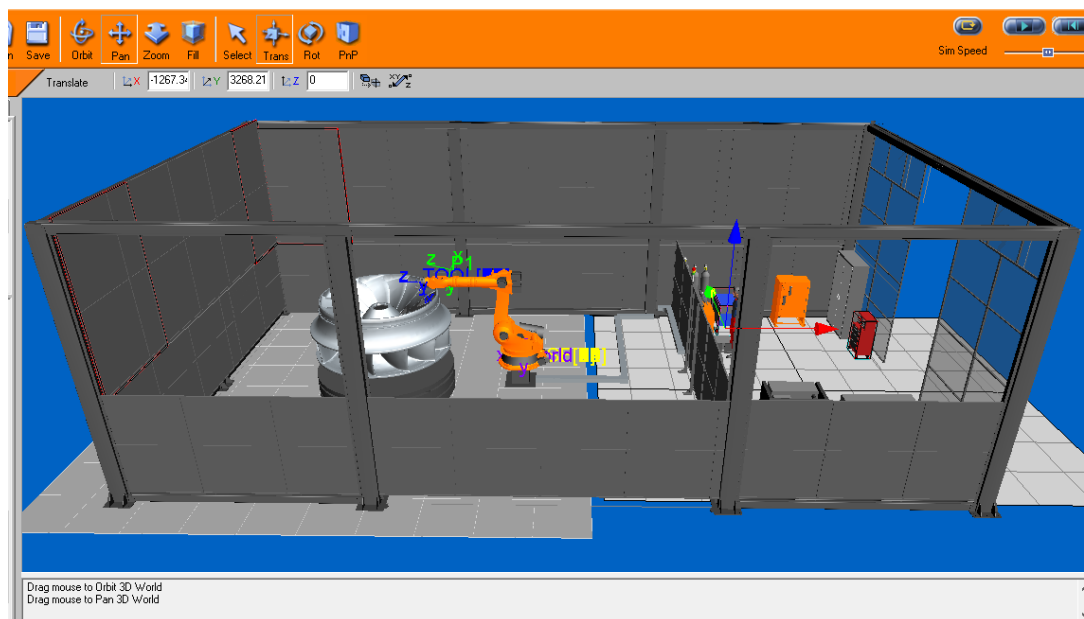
Vista frontal de la cabina de metalizado. (Fuente: Autor)
